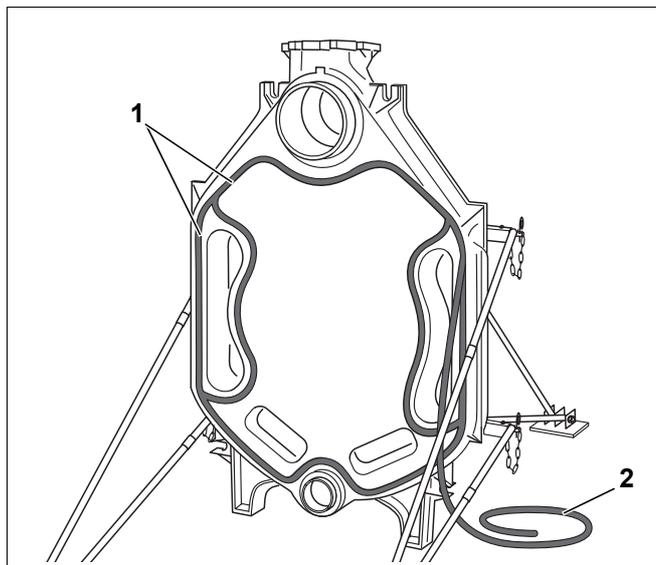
Dichtschnur (KM-Schnur) einsetzen
